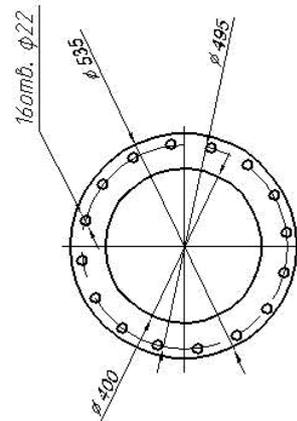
Габаритные размеры воздухоудки ТВ-175-1,6, газодудки ТГ-170-1,7
